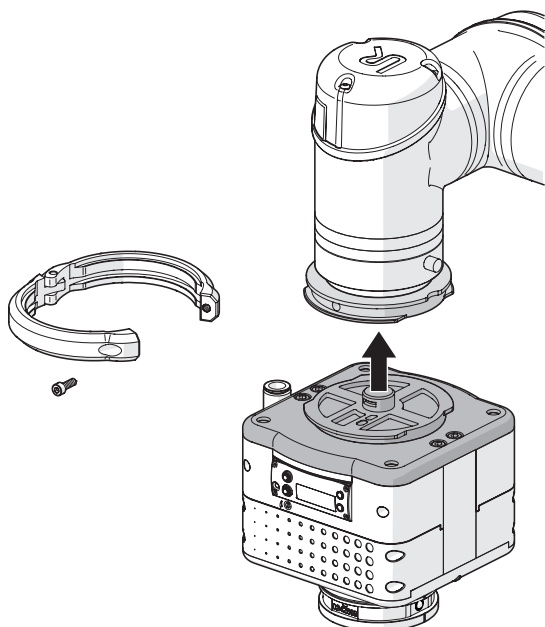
Die Adapterplatte wird mit 4 Schrauben und einem Führungsstift an einem Roboter befestigt.
